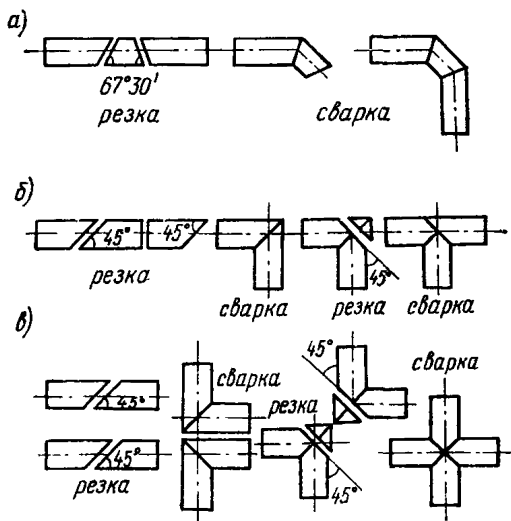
Схема процесса изготовления фасонных частей контактной стыковой сваркой
